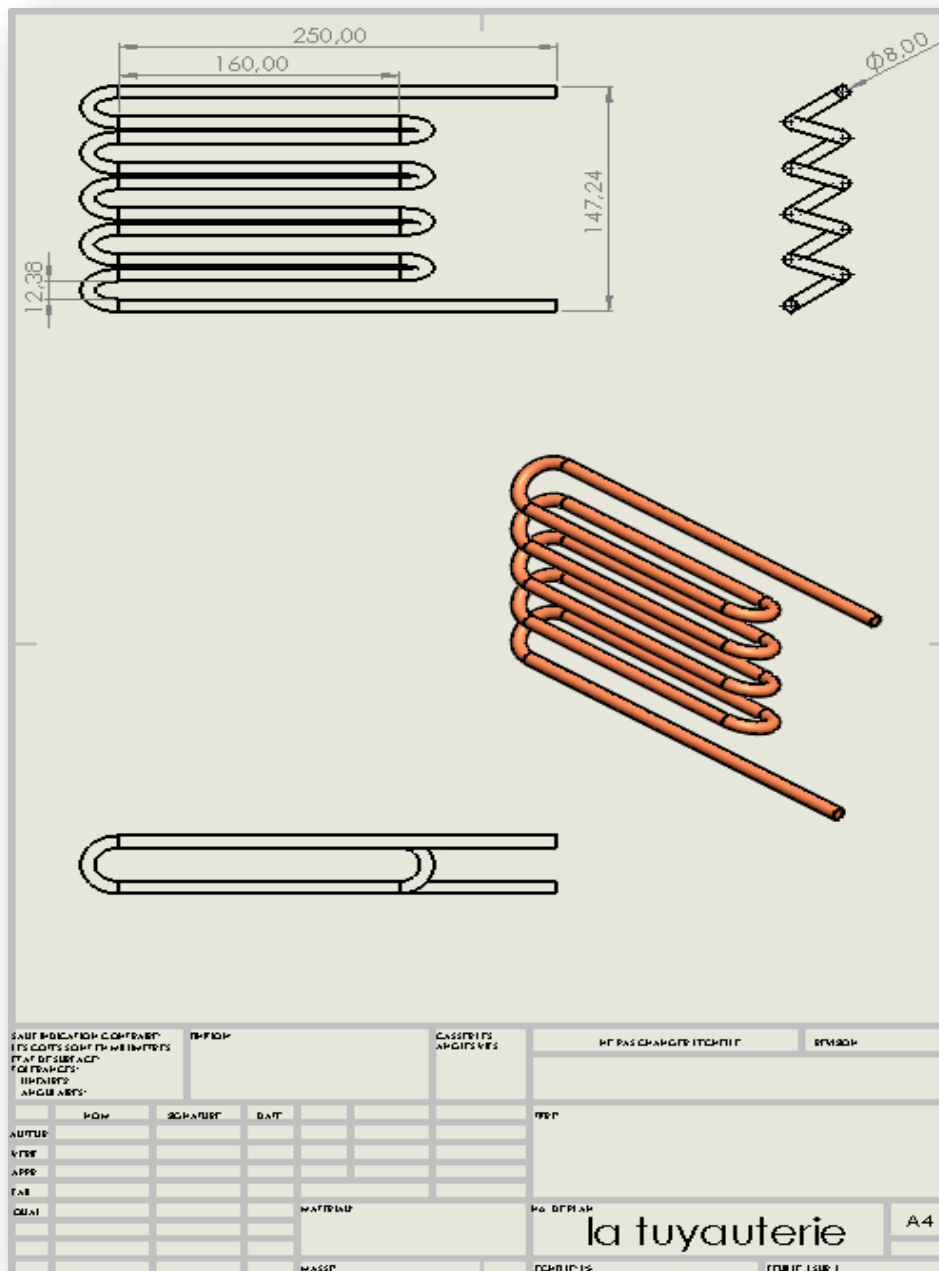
mise en plan de la vue éclatée du tube de circuit avec la CAO 3D.
